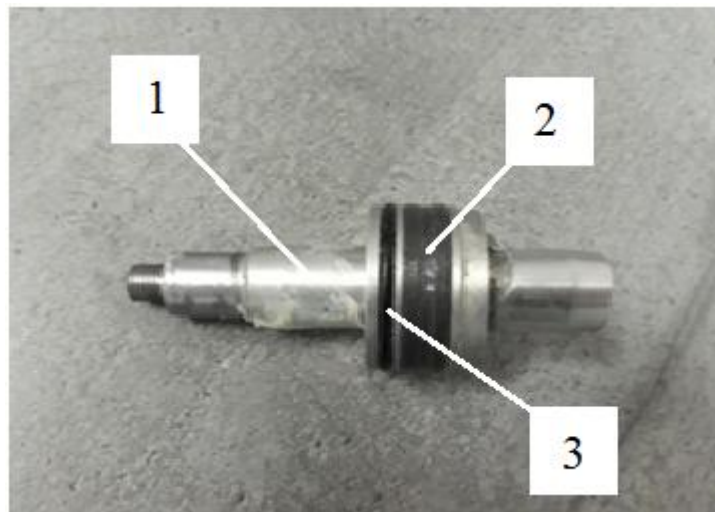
Загальний вигляд ударного поршня пневмомолота.
